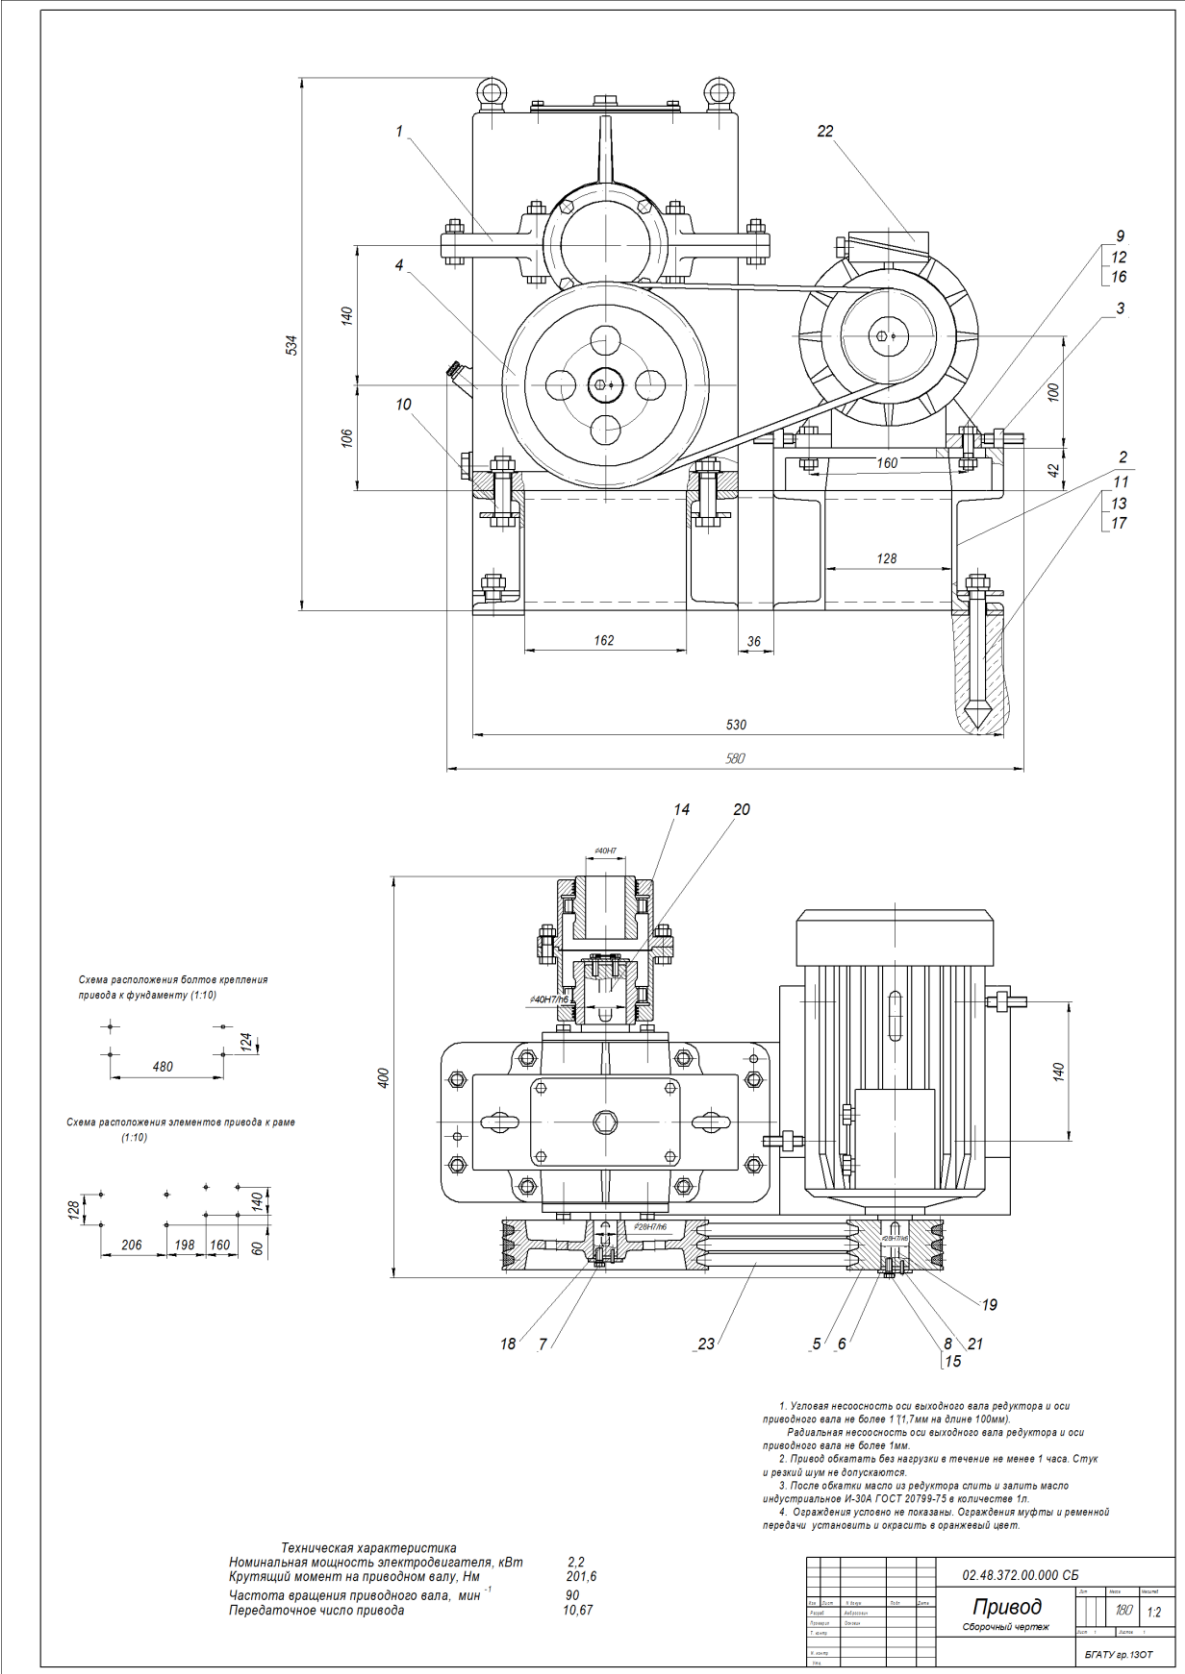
Станция приводная с цилиндрическим вертикальным редуктором и ременной передачей
